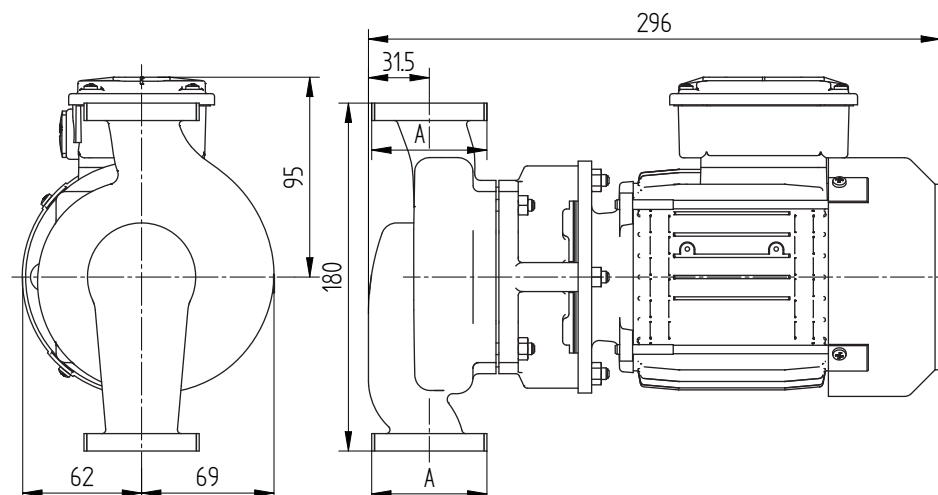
Размерный чертеж CL 4/4 и 5/4.
